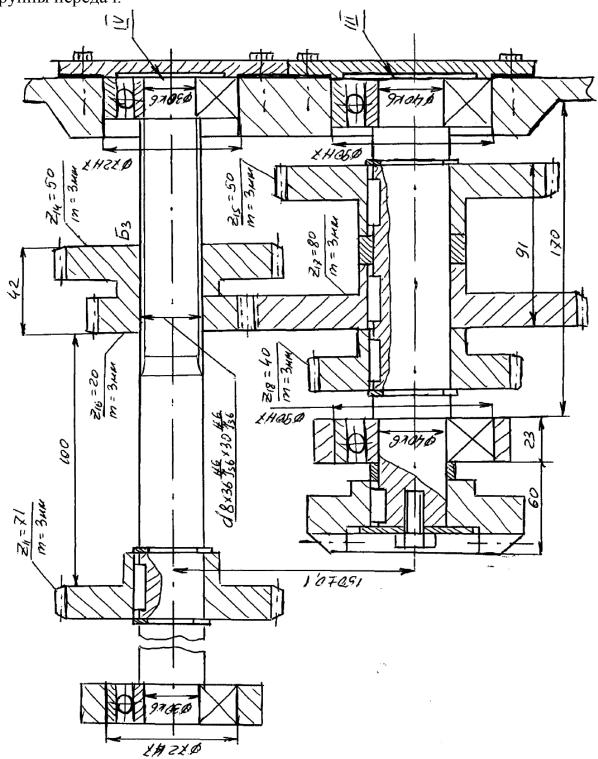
Сборочный чертеж наиболее нагруженной группы передач
